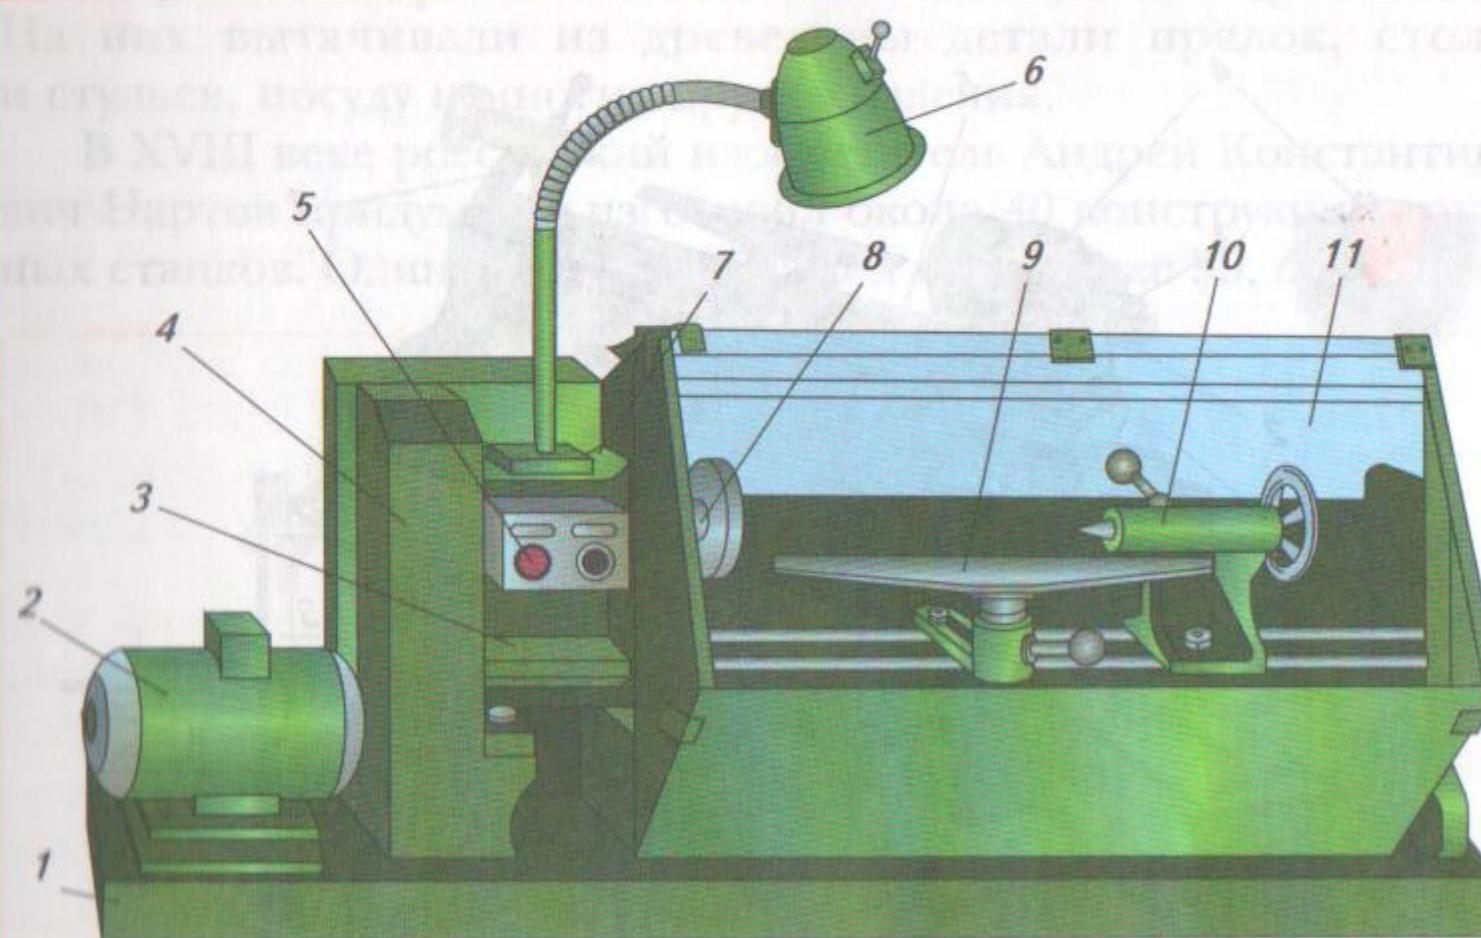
Токарный станок СТД-120 М для точения древесины: 1 — основание; 2 — электродвигатель; 3 — станина; 4 — ограждение ремённой передачи; 5 — кнопочная станция; 6 — светильник; 7 — передняя бабка; 8 — шпиндель; 9 — подручник; 10 — задняя бабка; 11 — защитный экран
